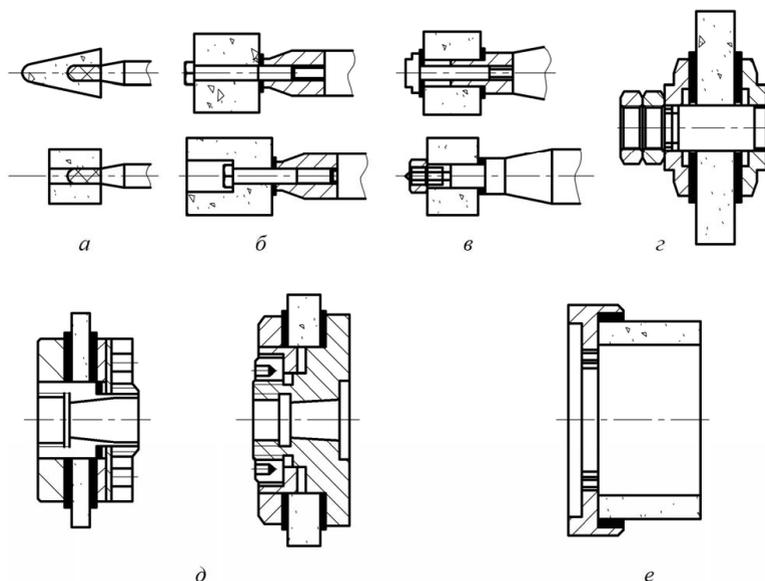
Конструкции устройств для крепления шлифовальных кругов: *а, б, в* – для внутреннего шлифования; *з, д* – для круглого и плоского шлифования; *е* – для шлифования торцом круга
